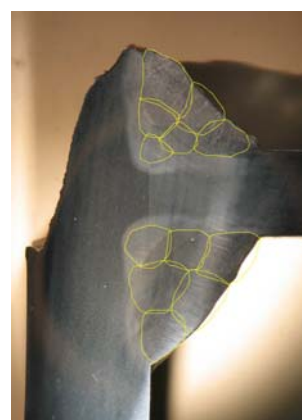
Idealização dos cordões de soldadura
